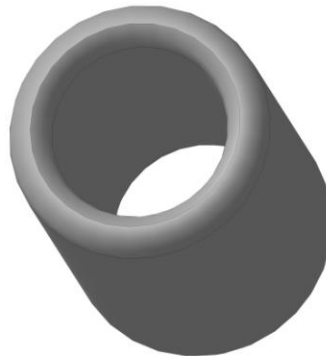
Заготовка деталі «Циліндр» у КОМПАС 3D
